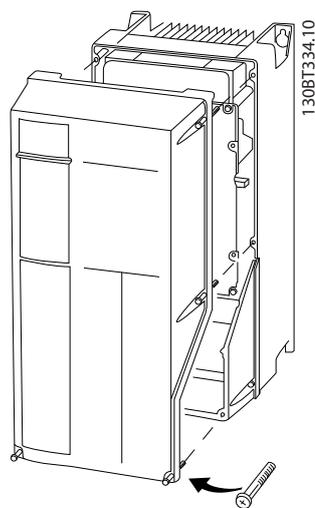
Acceso al cableado de las protecciones IP55 e IP66
